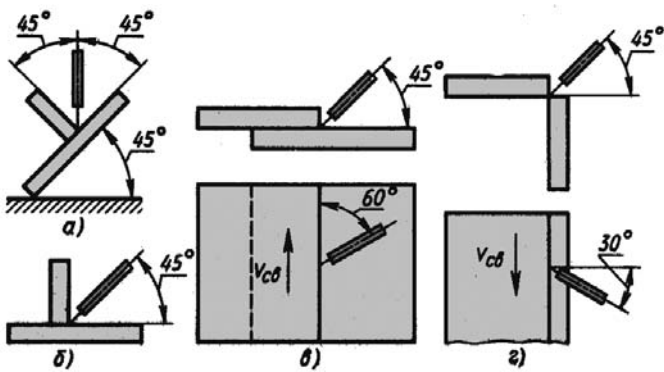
Положение электрода и изделия при сварке; а – в лодочку; б – таврового соединения; в – внахлестку; г – углового соединения
